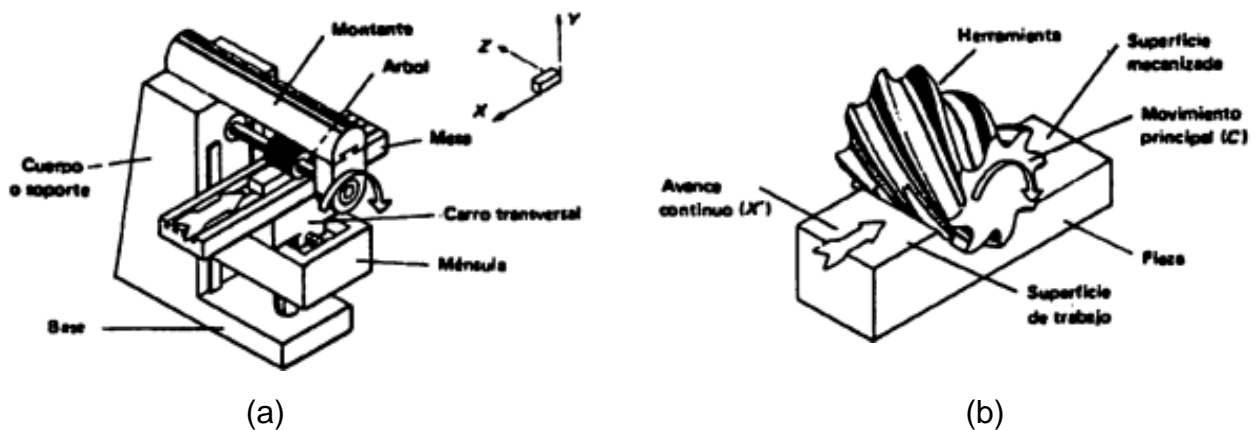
(a) Fresadora horizontal. (b) Movimientos en el fresado cilíndrico o periférico [10].
